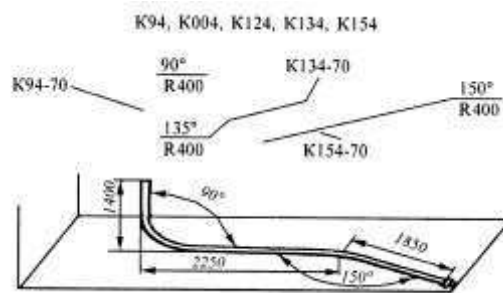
Елементи трубних заготовок, зігнутих під різними кутами
